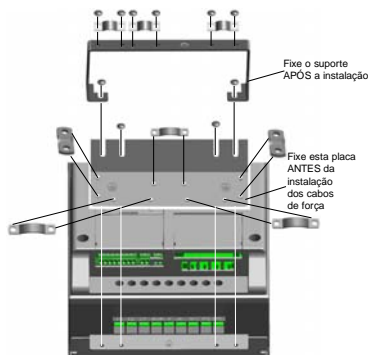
Instalação da placa PE e suporte a cabo API, MI4 - MI5
